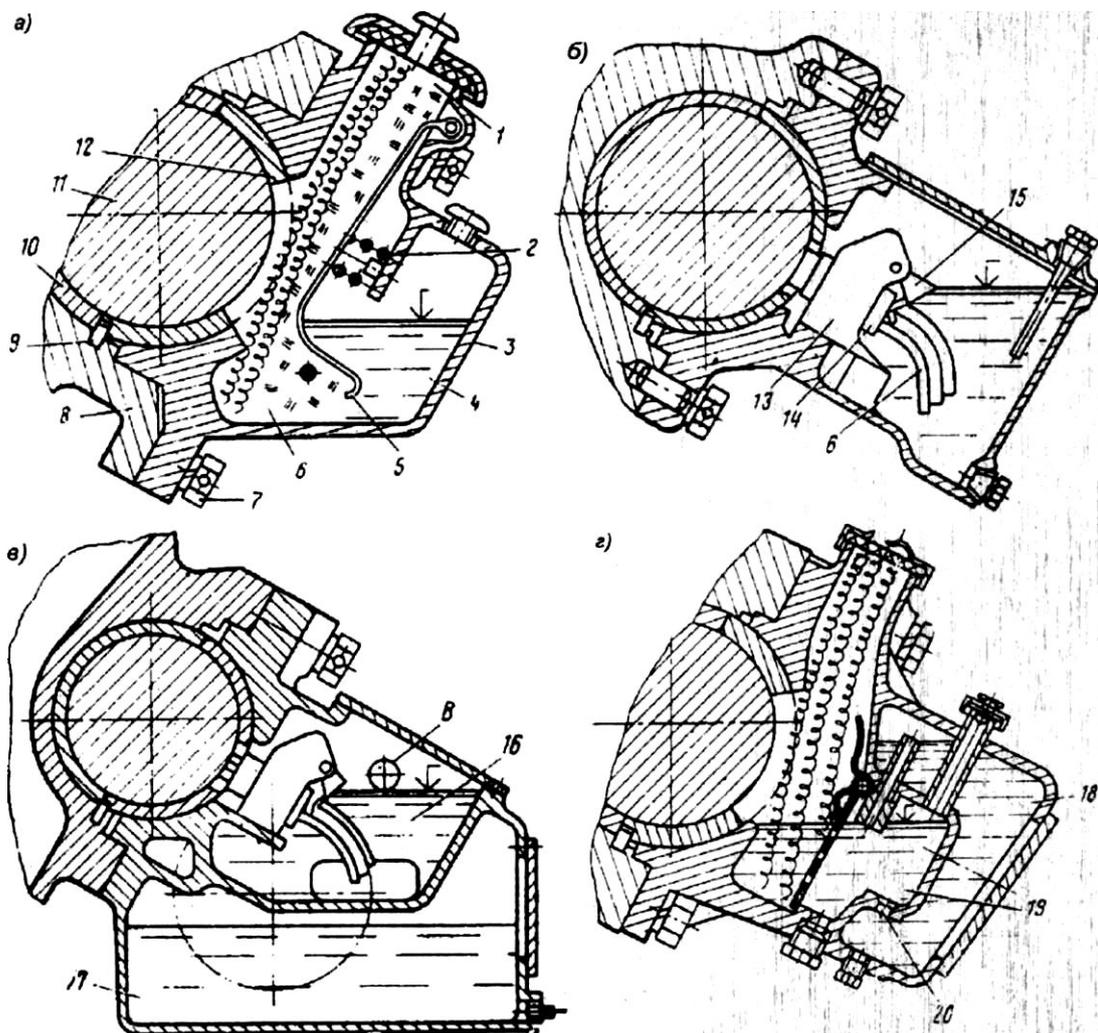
Моторно - осевые подшипники скольжения ТЭД в приводах класса I, с фитильной (а), пальстерной (б), циркуляционной системой (в) и с системой постоянного уровня смазки (г): 1-предохранительная набивка; 2-пружина; 3-шпунка; 4-смазка; 5-прижимная пластина; 6-фитиль; 7-болт; 8-остов двигателя; 9-шпунка; 10,12-баббитовые вкладыши; 11-ось колесной пары; 13-остов; 14-коробка; 15-рычаг; 16-верхние камеры; 17-маслосборник; 18,19-камеры; 20-отверстие;
